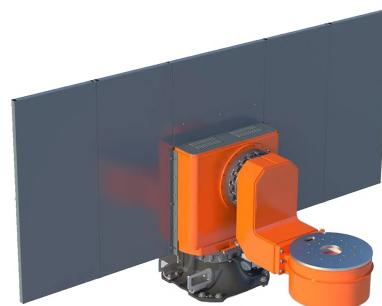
Dumeta 4–Axis Hydraulic Elevating Positioner. [5]
